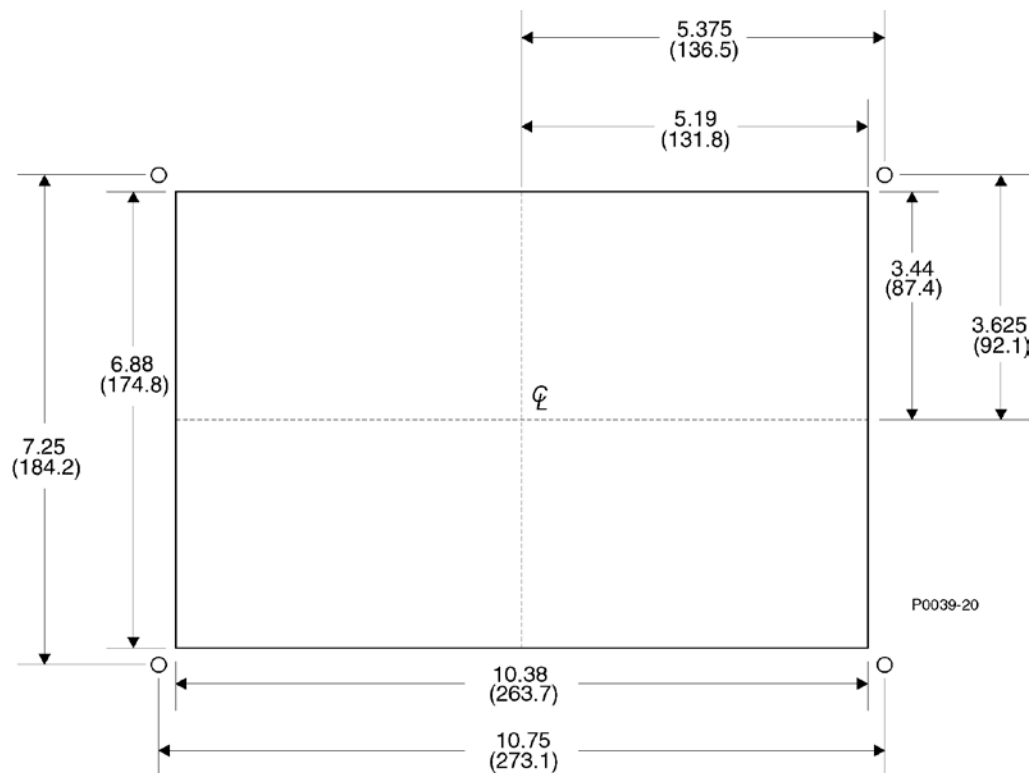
Dimensiones de Corte de Perforación del Panel
